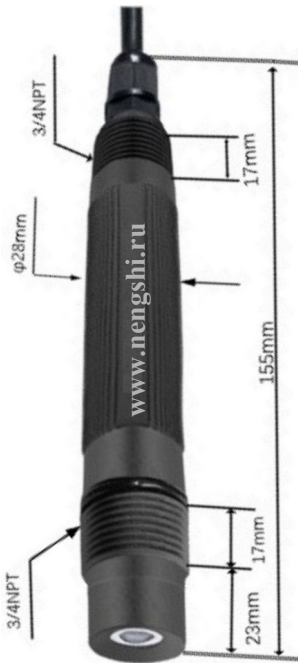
Тип корпуса «S». Материал PPS. FLAT, встроенный кабель
